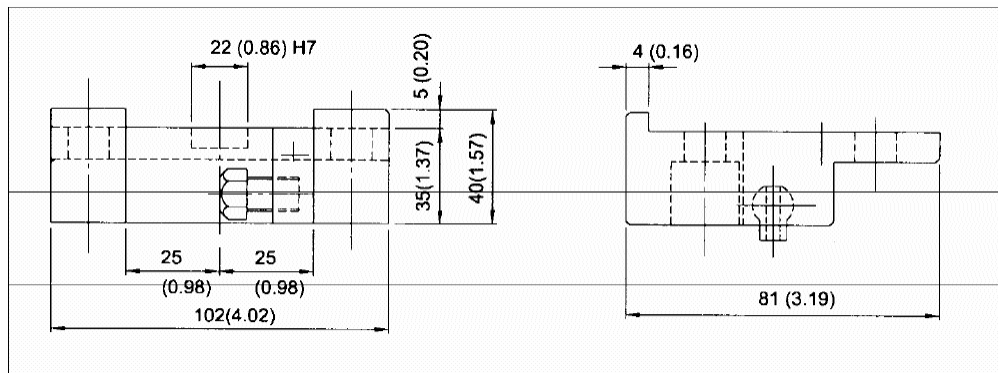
Габариты резцедержателя (резцедержатель типа I внешнего диаметра)
